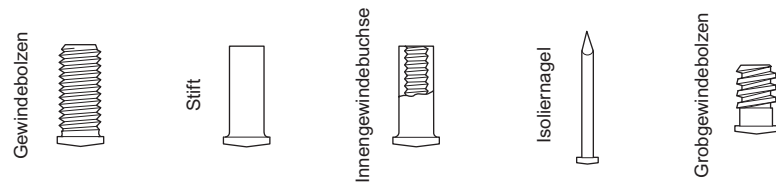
7 Einige Beispiele verschiedener Ausführungen von Schweißelementen für Short Cycle
